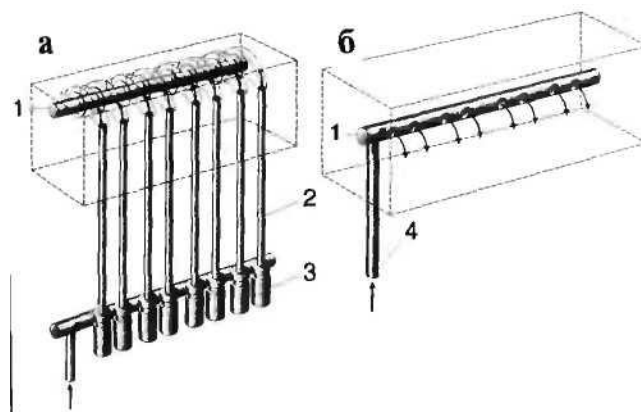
Вигляд типового рішення надходження моторного масла в голівку блоку циліндрів з нижнім розподільним валом (ОНV): а - через гідроштовхальники і штанги; б - через спеціальний канал; 1 - вісь коромисел; 2 - штанга; 3 - гідроштовхальник; 4 - вертикальний канал, що подає
